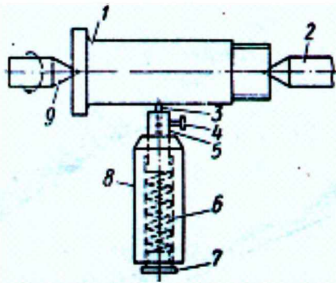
Схема фрикционного омеднения стальной детали: 1 – деталь, подвергающаяся меднению; 2 – подвижной центр задней бабки станка; 3 – медный пруток; 4 – винт для закрепления медного прутка; 5 – плунжер; 6 – пружина; 7 – резьбовая пробка; 8 – корпус приспособления, закрепленный в резцедержателе станка; 9 – центр, закрепленный в патроне
